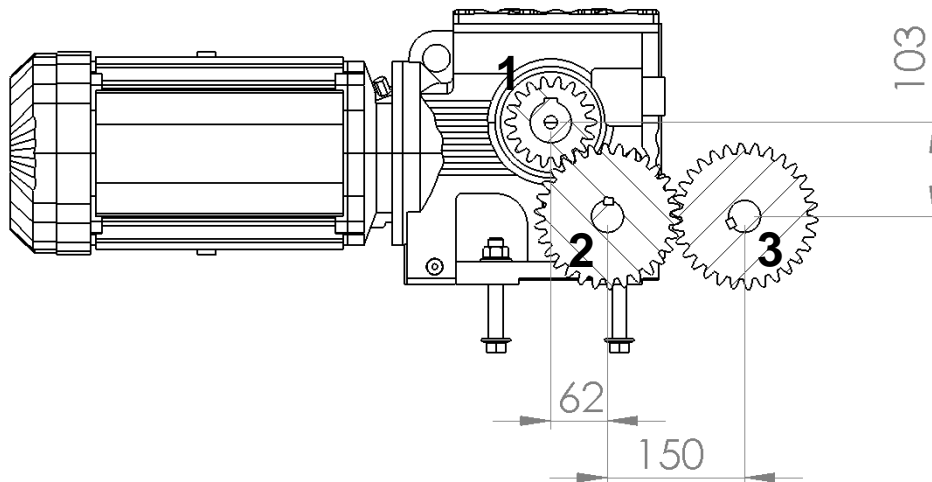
Dimensões entre veios do trem de engrenagem e numeração das rodas dentadas
